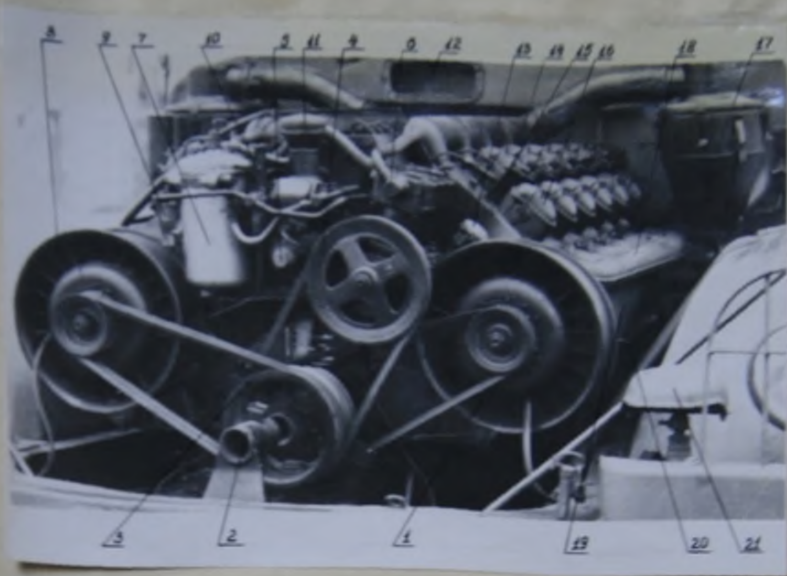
Двигатель Татра III-A. Вид спереди слева.
